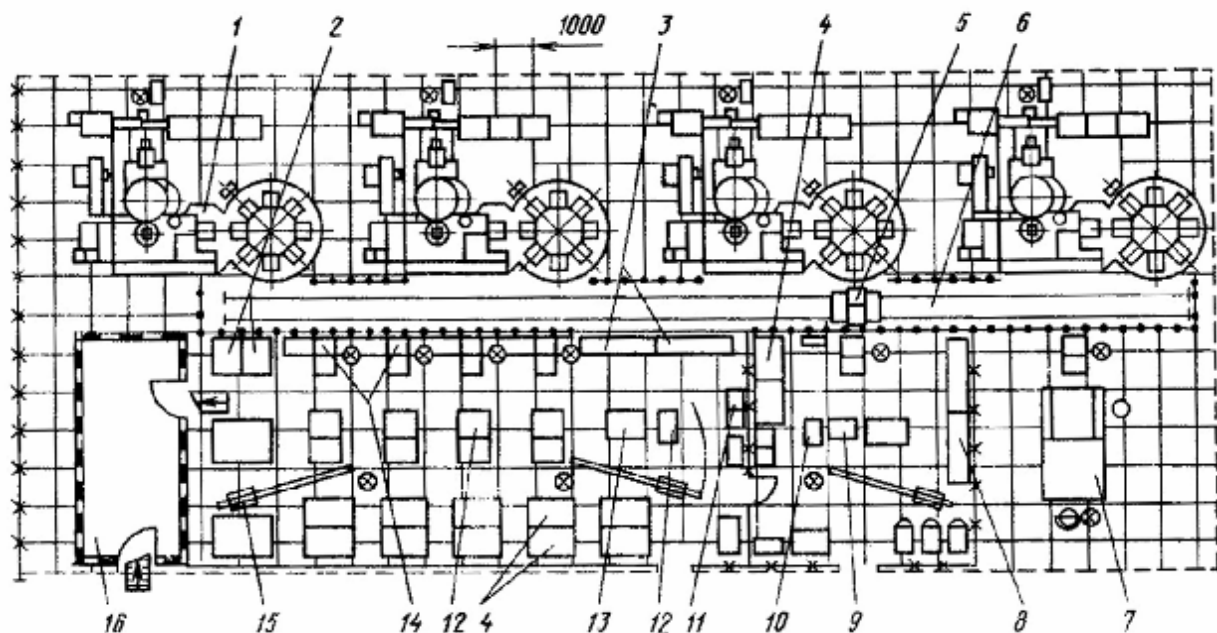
Планировка ГПС АСК-20 для изготовления корпусных деталей станков в условиях мелкосерийного производства
